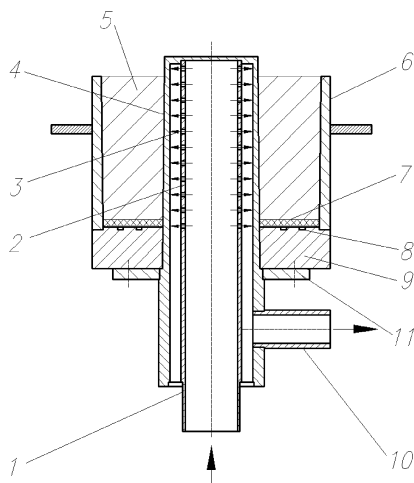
Схема опытной установки: 1 – подводщий патрубок; 2 – экран; 3 – затопленные струи; 4 – стальной стержень; 5 – отливка; 6 – съемный захват; 7 – графитовая вставка; 8 – паз; 9 – основание; 10 – отводящий патрубок; 11 – фланец
